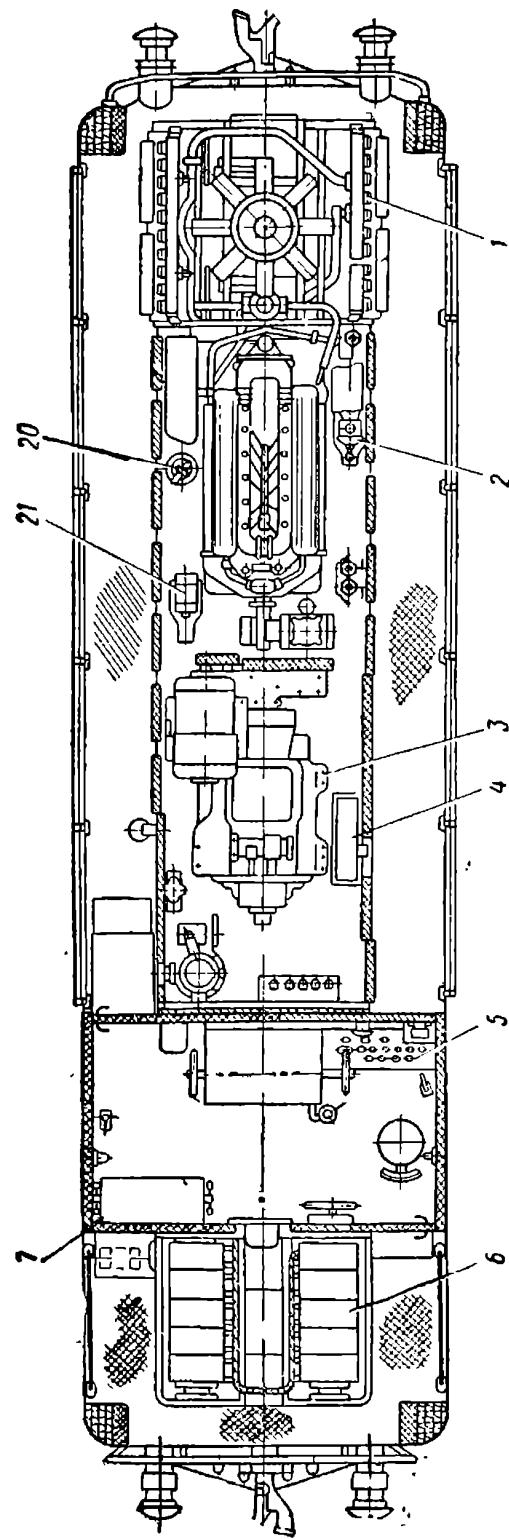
Продольный разрез и план тепловоза ТГМ3:
